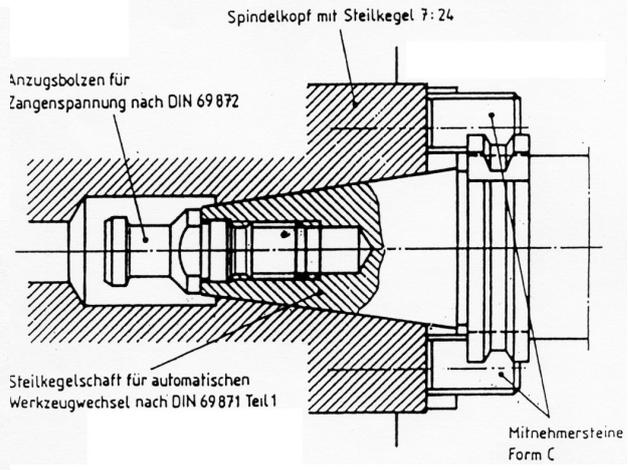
Spindel-Werkzeug-Schnittstellen bei Fräsmaschinen, Steilkegel für niedrige bis mittlere Drehzahlen
